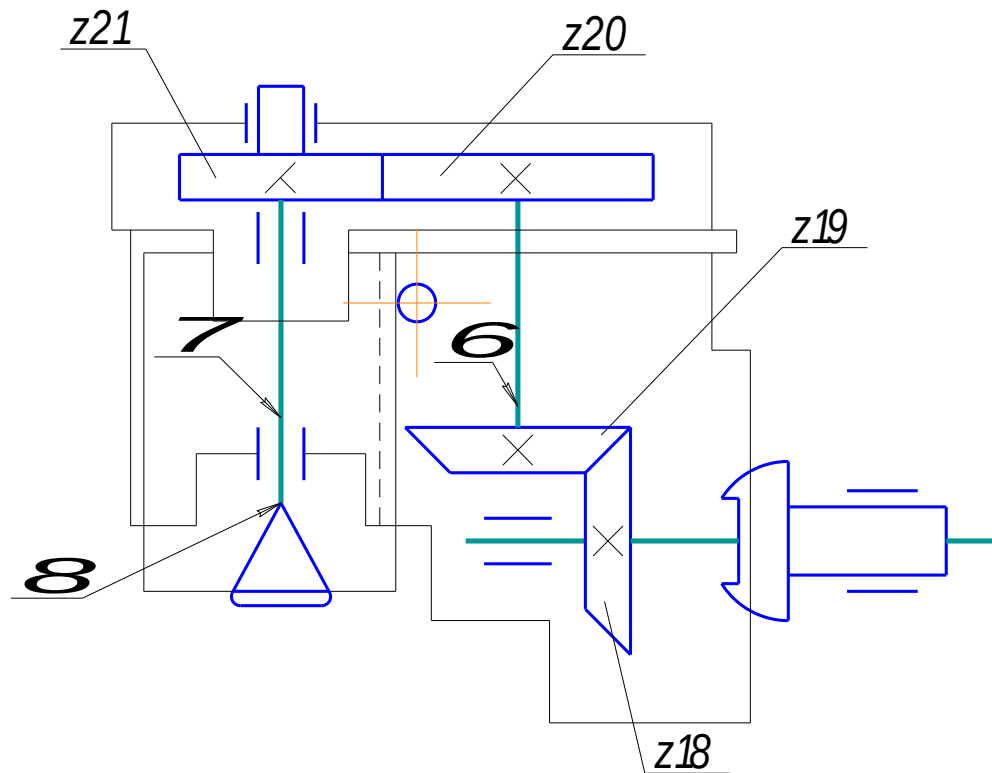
Конічна передача 18/19 у коробці швидкостей широко-універсального фрезерного верстата.
